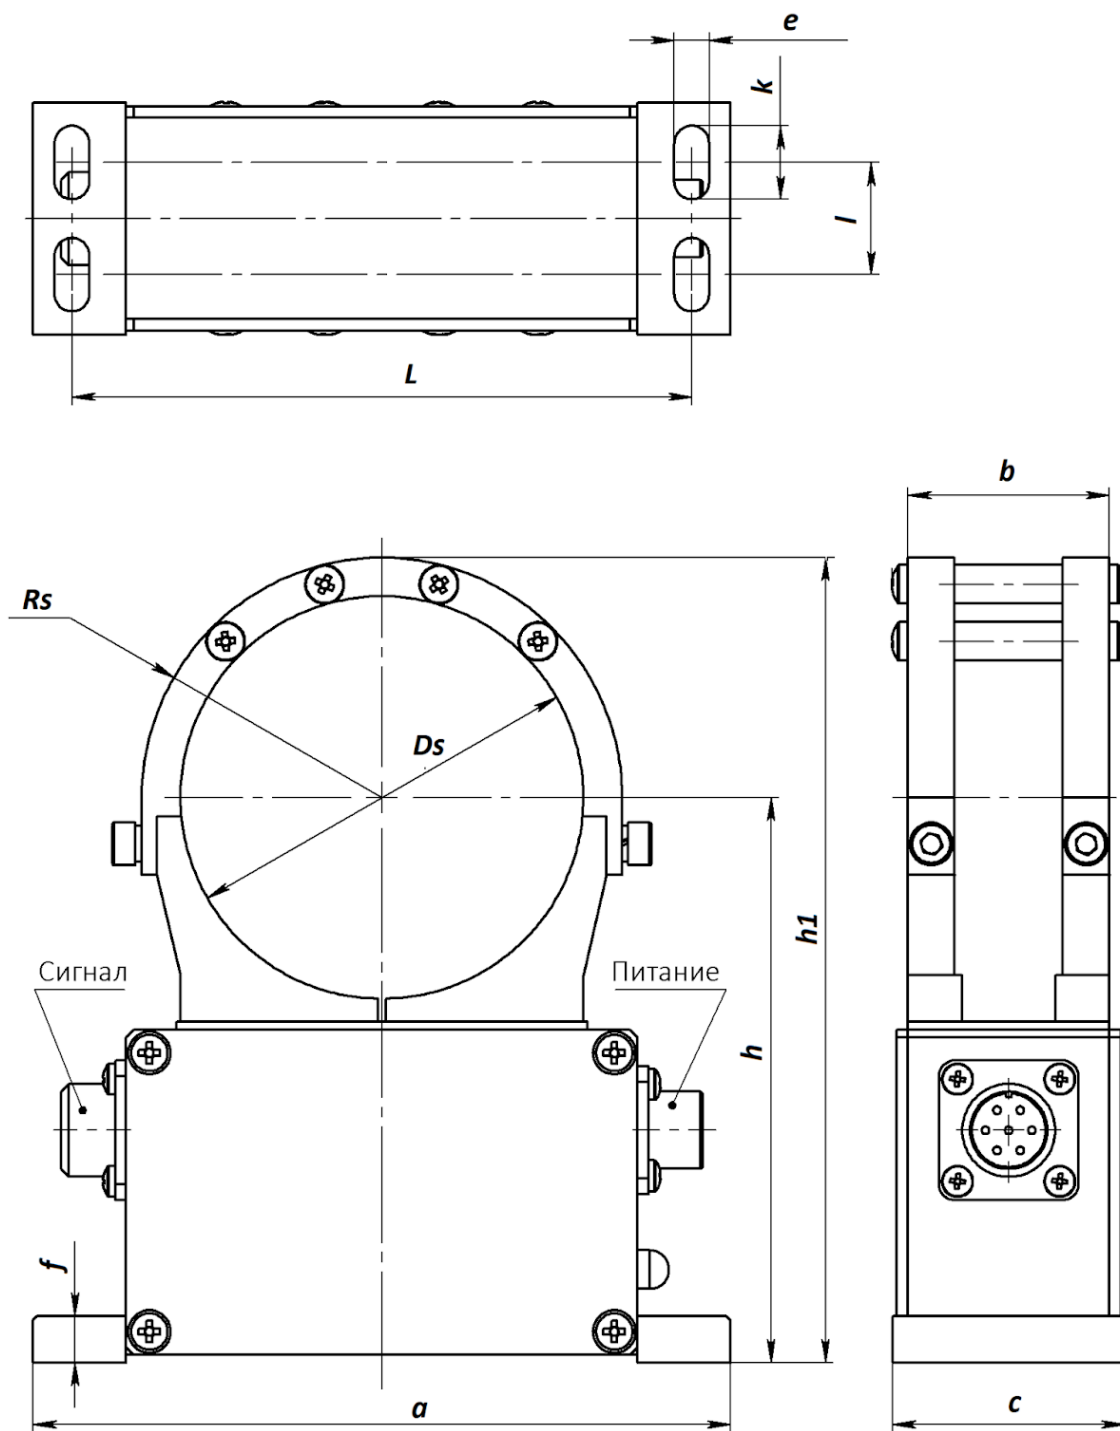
Статор ТТ020.01.00.00-XXX Габаритные и установочные размеры, мм.
